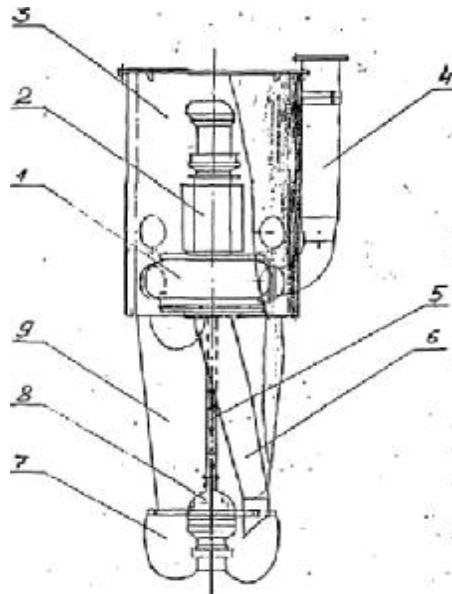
Универсальный землесосный модуль с фрезерным рыхлителем:
